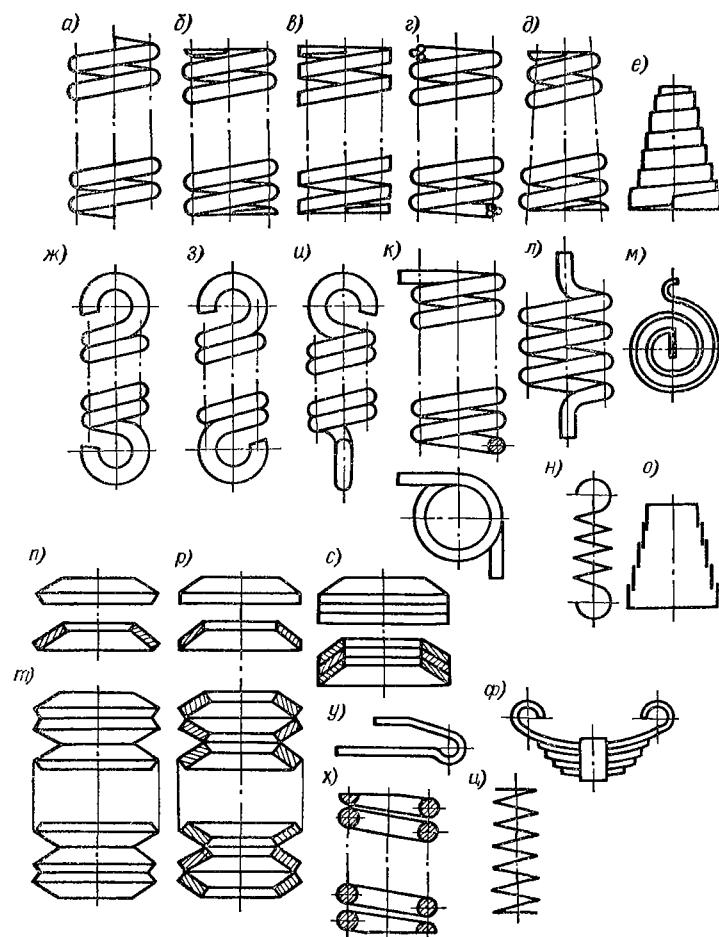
Условные изображения пружин на чертежах сборочных единиц
